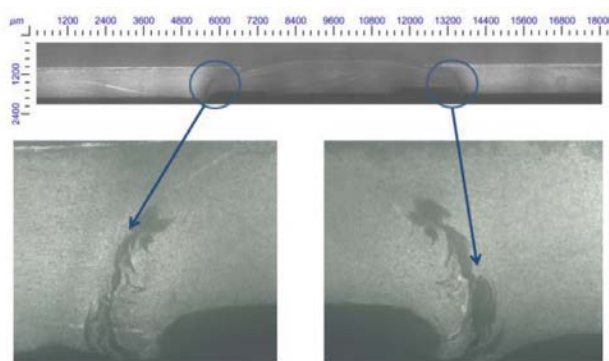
Микроструктура сварного соединения образца № 3 с непроваром по кромке сварного соединения.
